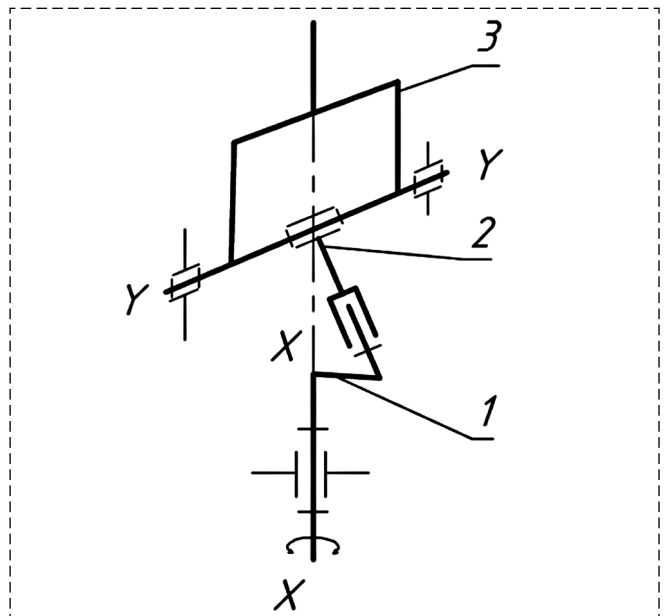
Кинематическая схема механизма с качающейся шайбой и косым кривошипом
